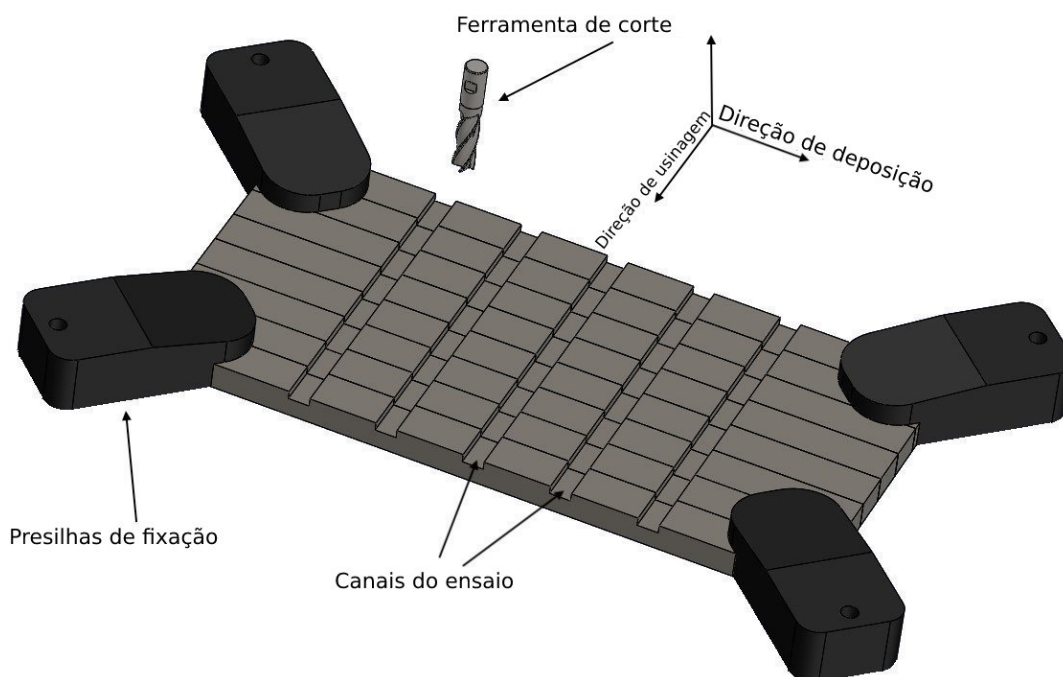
Representação do processo de usinagem da peça na fresadora CNC.
